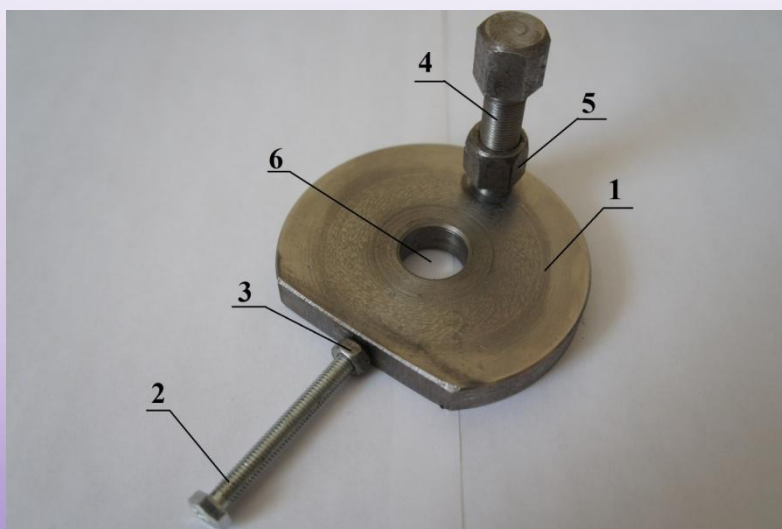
Конструкция регулируемого болтового тормоза:
